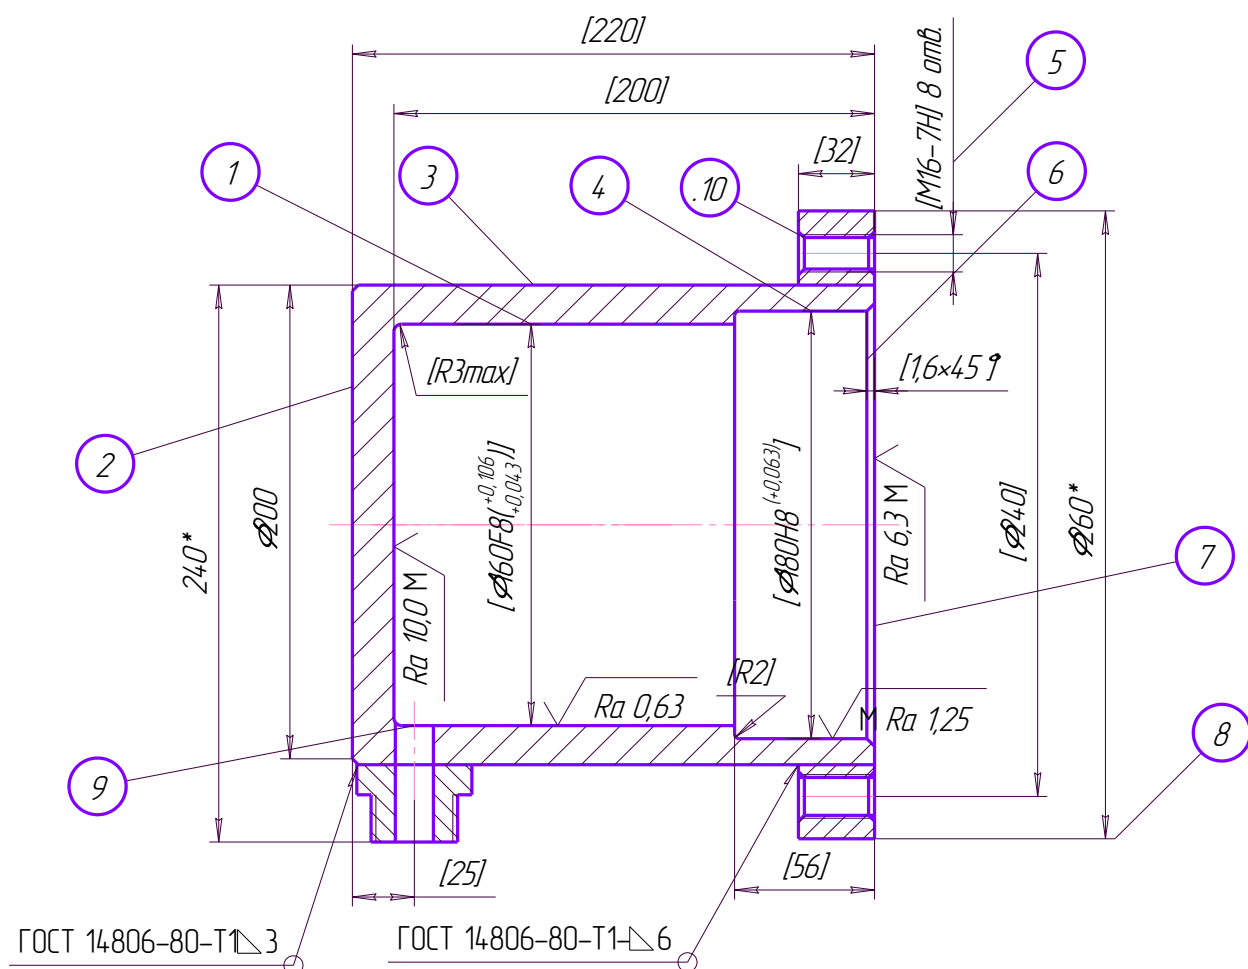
Эскиз детали «Цилиндр» после сварки
